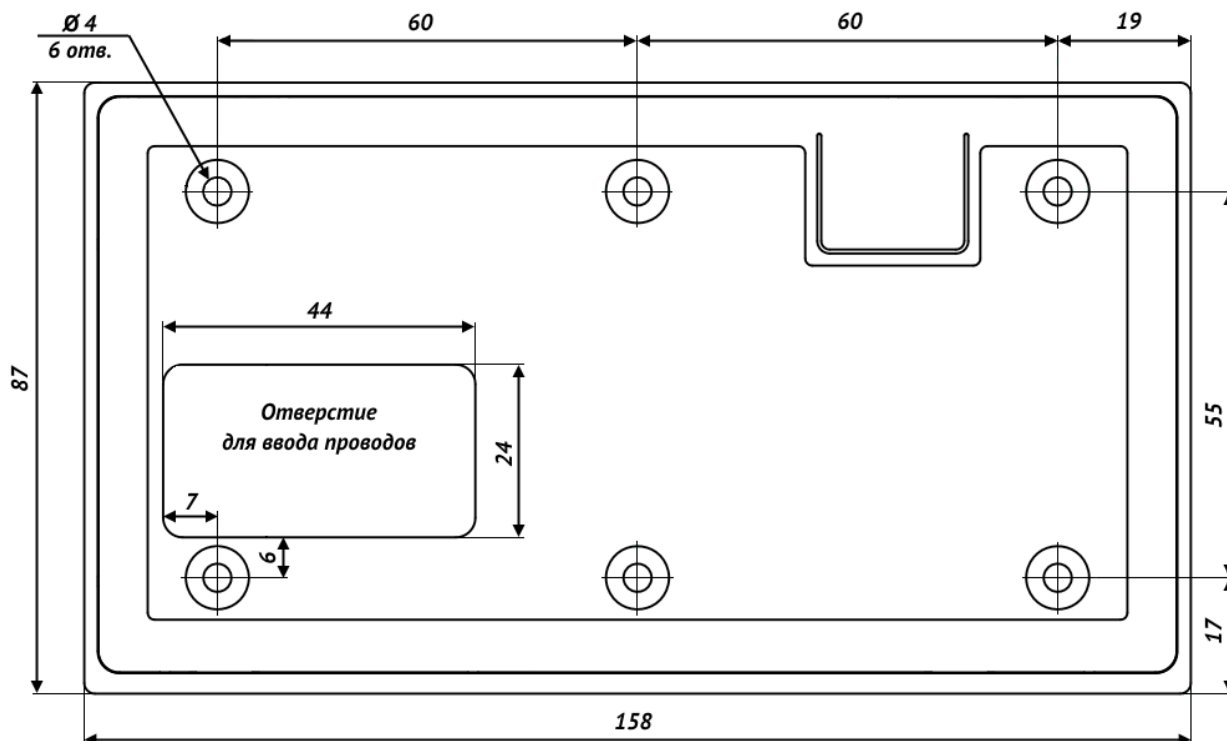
Габаритные и присоединительные размеры УИУ (вид с обратной стороны)
